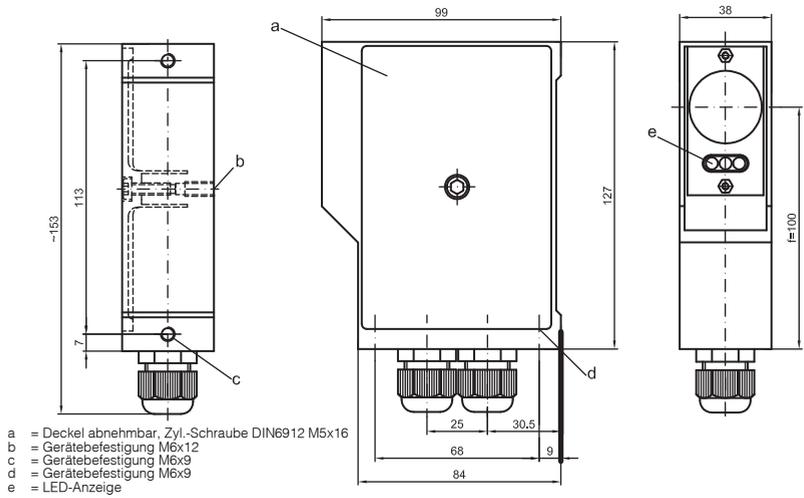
SLS 78/R mit PG-Verschraubung
